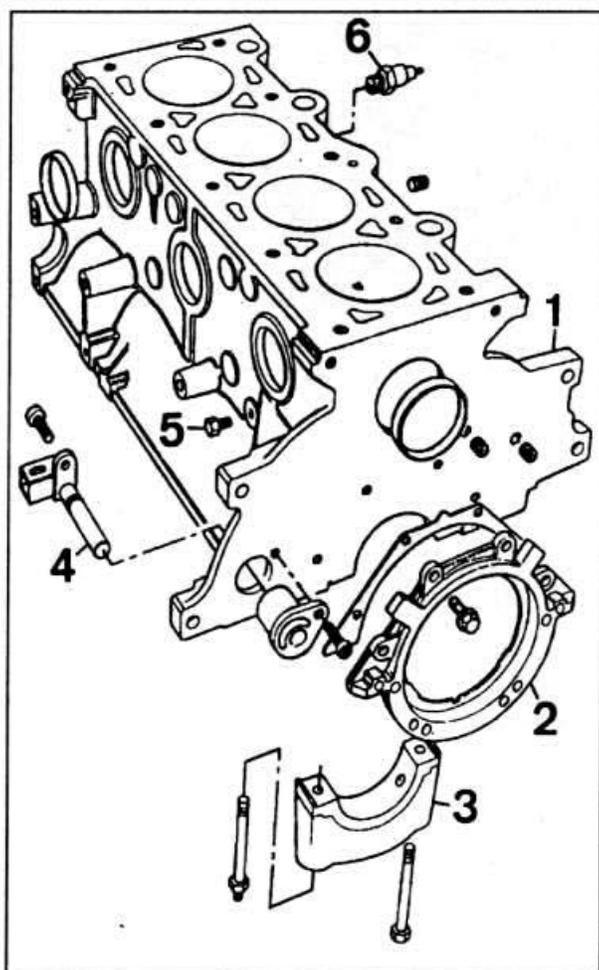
D.53. Блок цилиндров двигателя Zetec.
